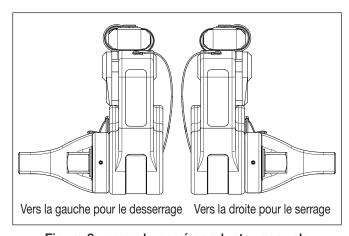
sens du carré conducteur pour le desserrage/serrage
